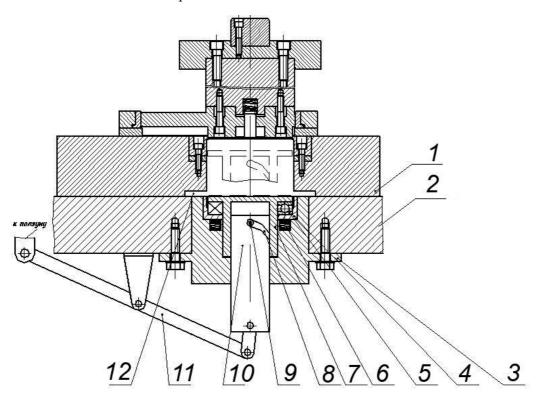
Устройство поворота вырубленной заготовки на 90°.
